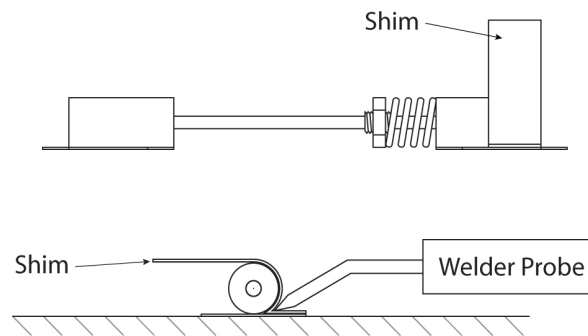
Soldado de la calza de ajuste del collarín en su lugar
